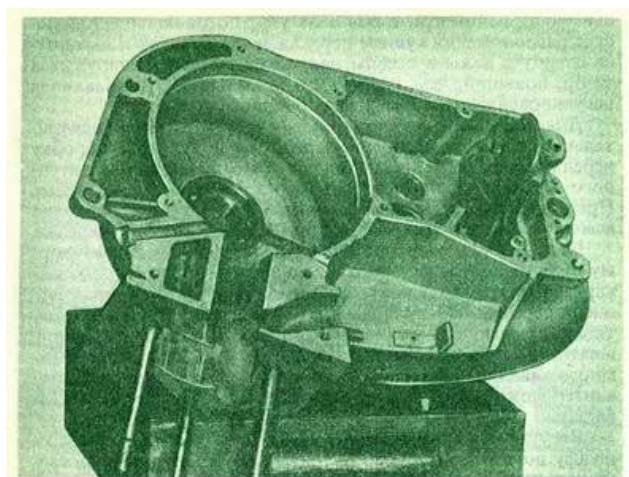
Левая половина картера двигателя, подготовленная к сборке
